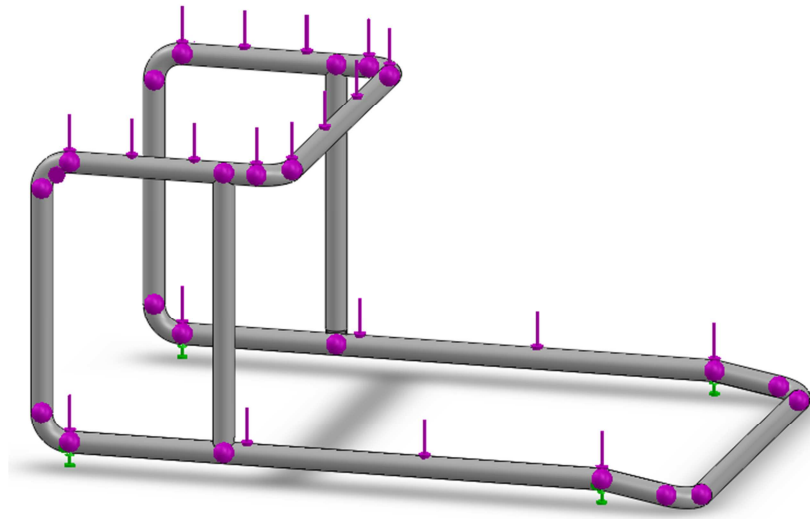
Geometrías fijas y cargas aplicadas a la estructura inferior.
